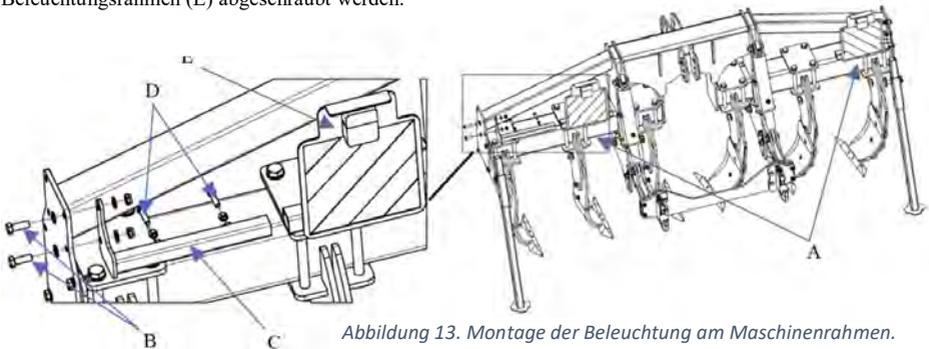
Montage der Beleuchtung am Maschinenrahmen.
